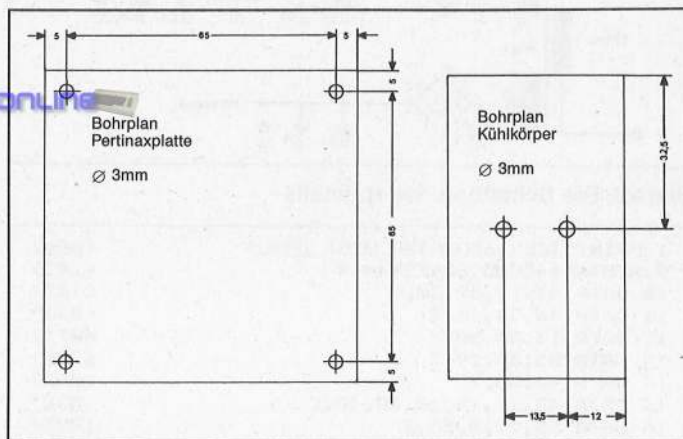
Die Bohrpläne für die die Pertinaxplatte und den Kühlkörper des Netzteils.
